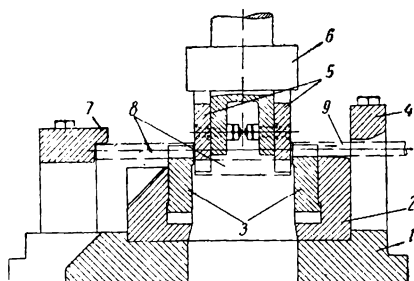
Схема двухопорного штампа для одновременной резки двух заготовок: 1 — нижняя плита; 2 — нижняя державка; 3 — нижние ножи; 4 — направляющая скоба; 5 — верхние ножи; 6 — верхняя державка; 7 — упор; 8 — заготовка; 9 — пруток
